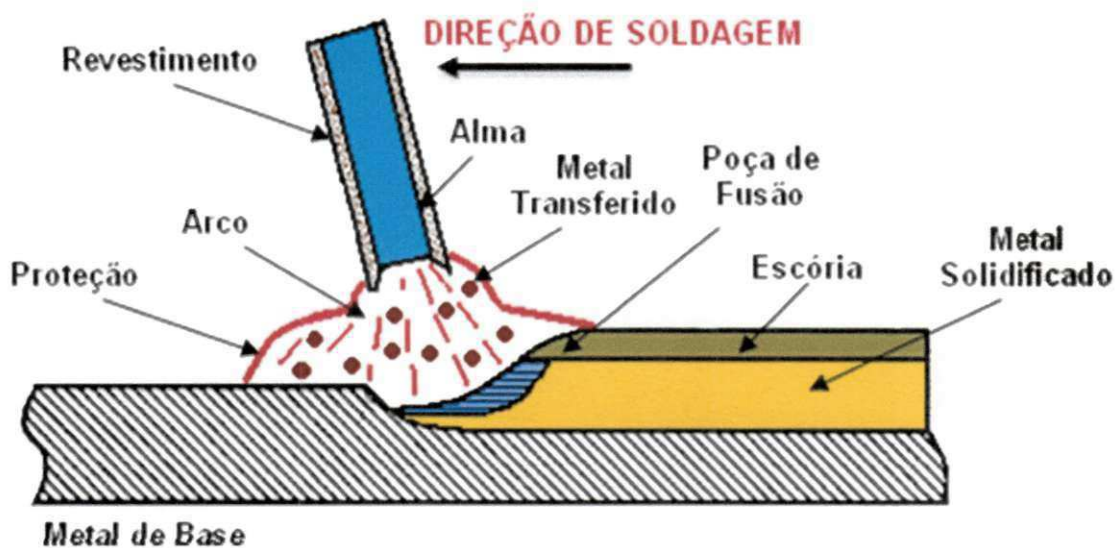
Soldagem por Eletrodo Revestido (SMAW).
